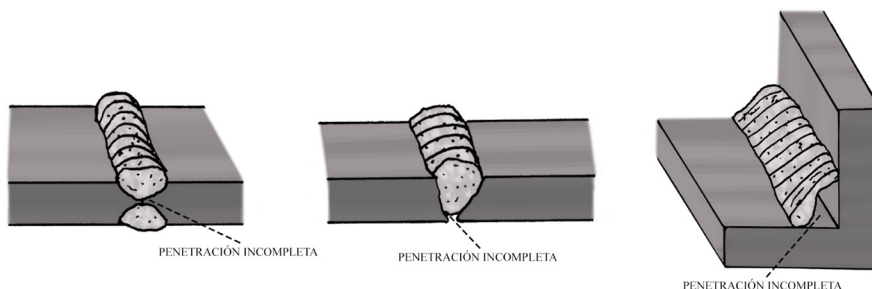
Defectos en la soldadura: penetración incompleta
